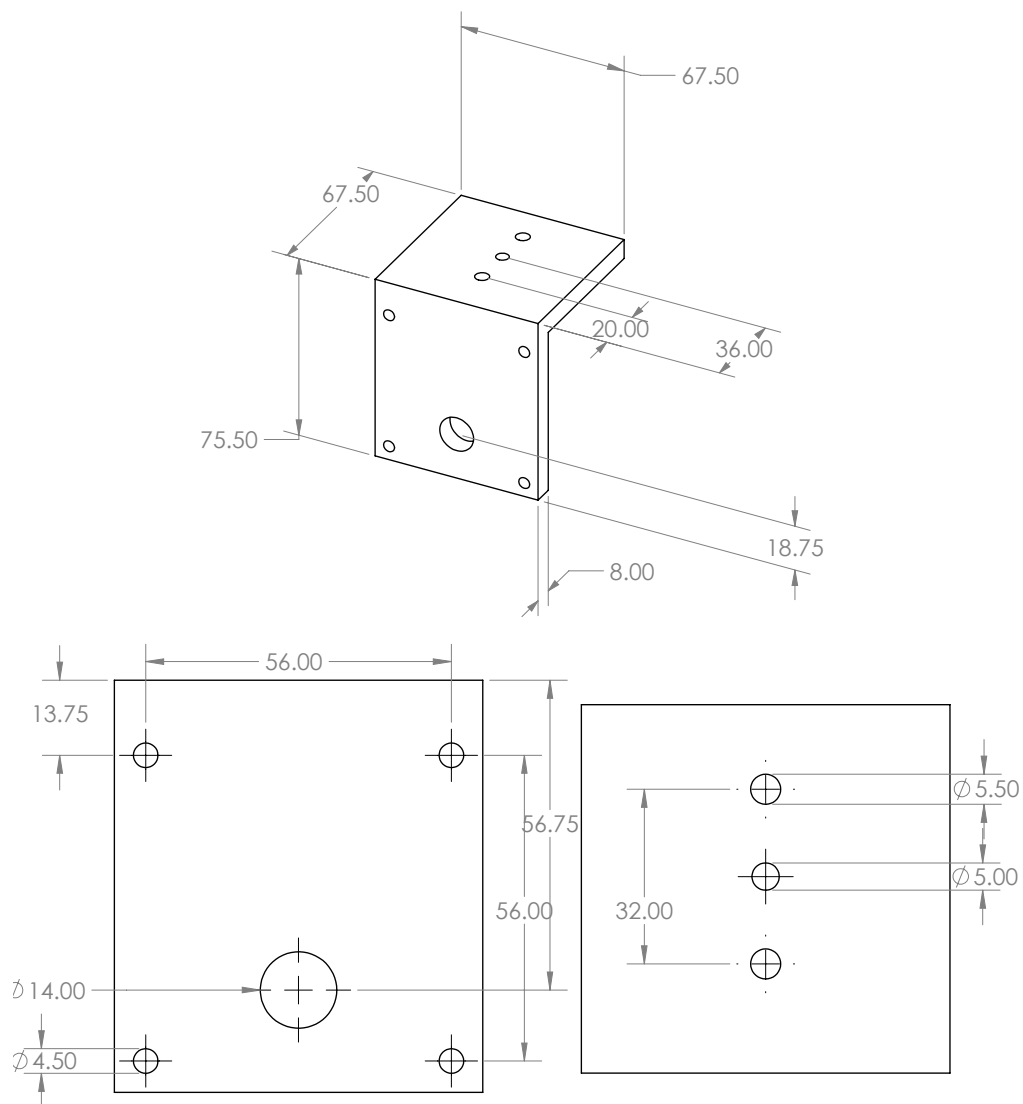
Mise en plan de la pièce cornière avec dimensions
